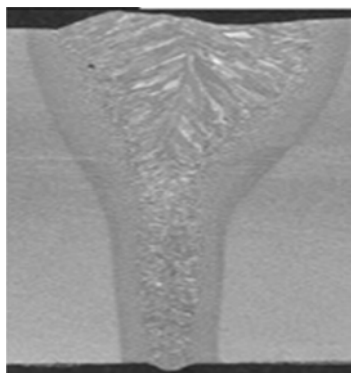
Микроструктура сварного соединения, полученного лазерной сваркой
